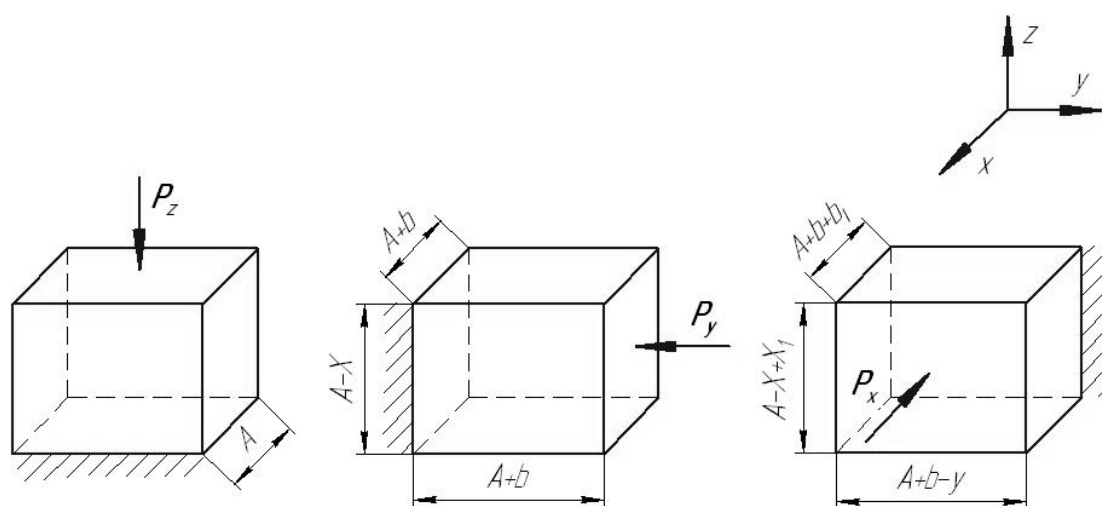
Способ всесторонней ковки кубической заготовки
